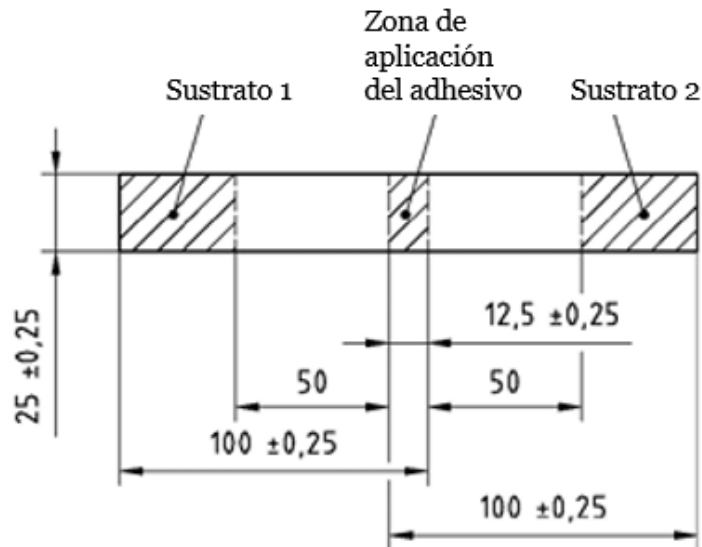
Vista en planta del esquema de medidas reguladas que deben tener las probetas según la norma (UNE-EN 1465, 2009).
